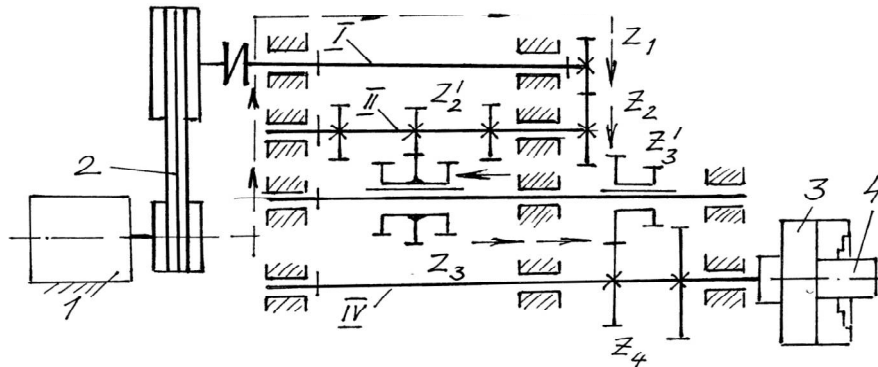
Кінематична схема проводу головного руху токарно - револьверного верстата мод.1336М
